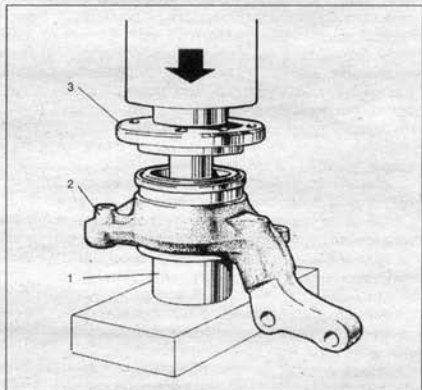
Запрессовка ступицы колеса: 1 – оправка; 2 – поворотный кулак; 3 – ступица
